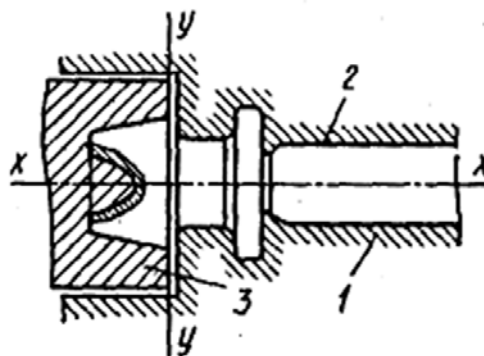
Схема штамповки на ГКМ: 1 – неподвижная часть матрицы; 2 – подвижная часть матрицы; 3 – пуансон
